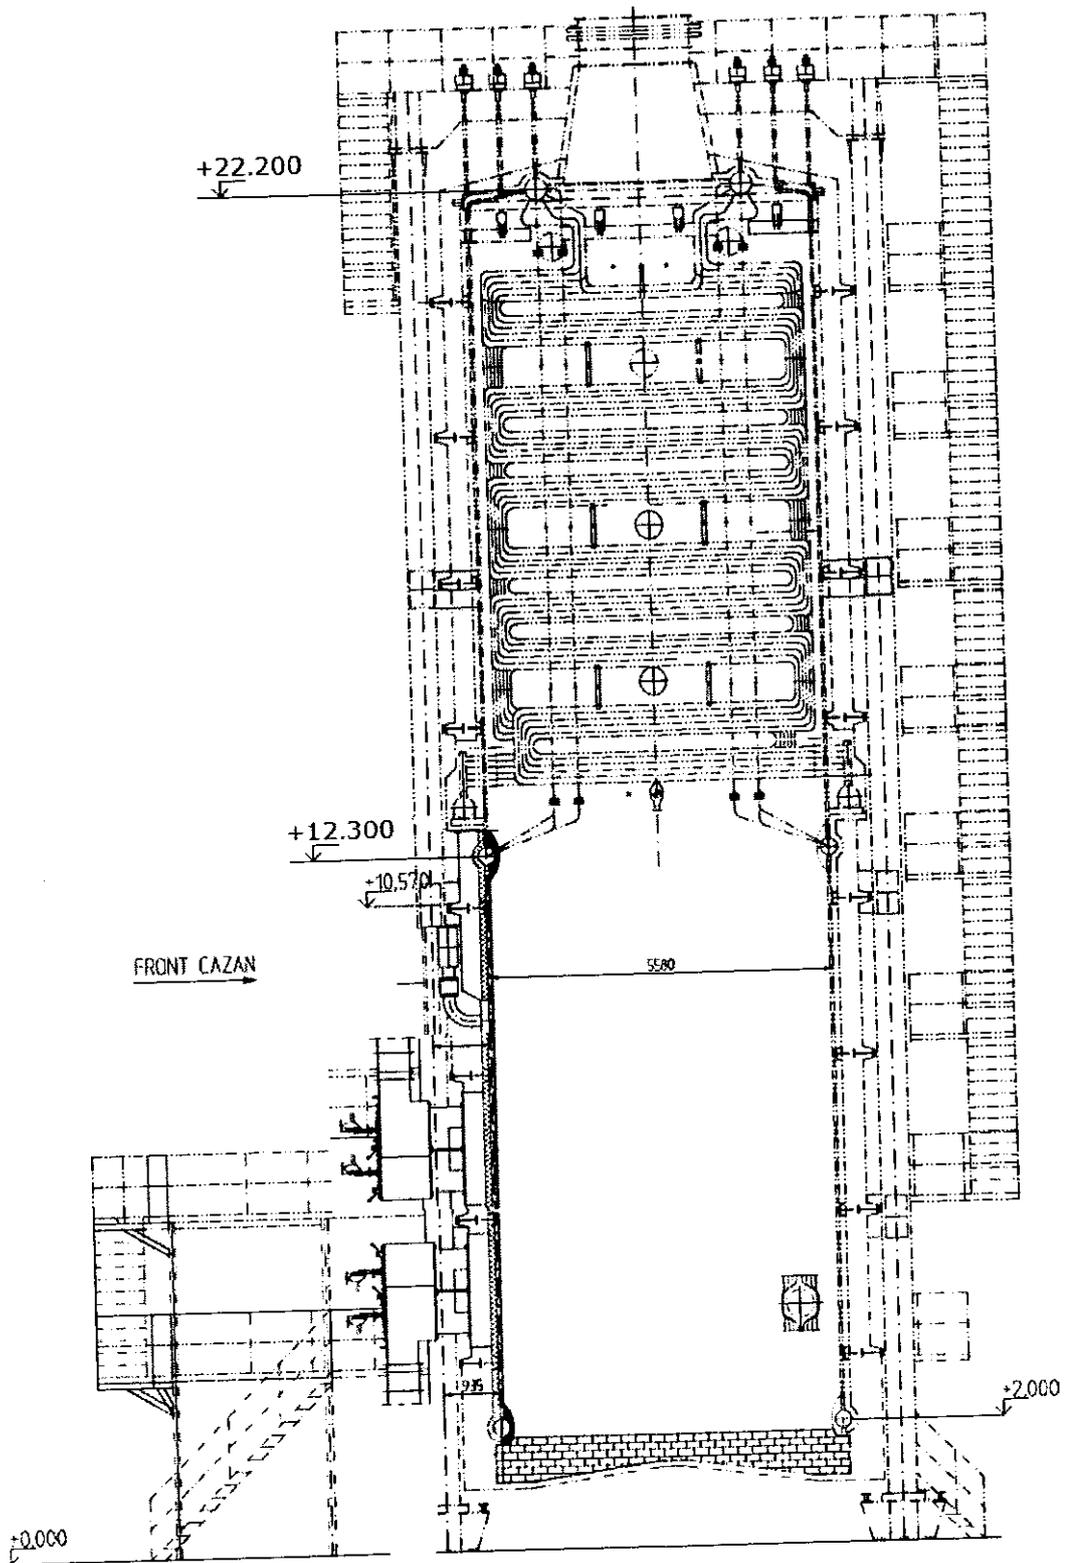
b.1.1.1 Secțiune schițată prin CAF 116 MW Bacău Letea
